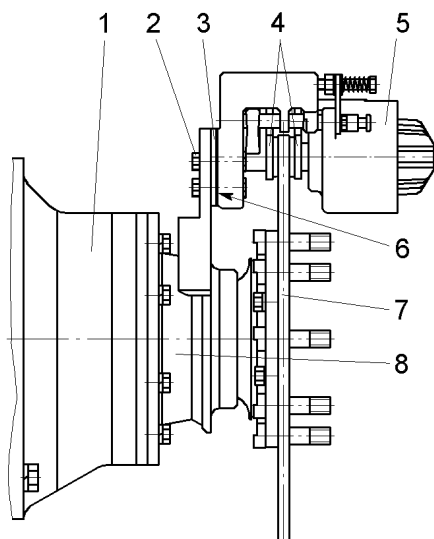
Снятие и установка стояночного тормозного механизма:
